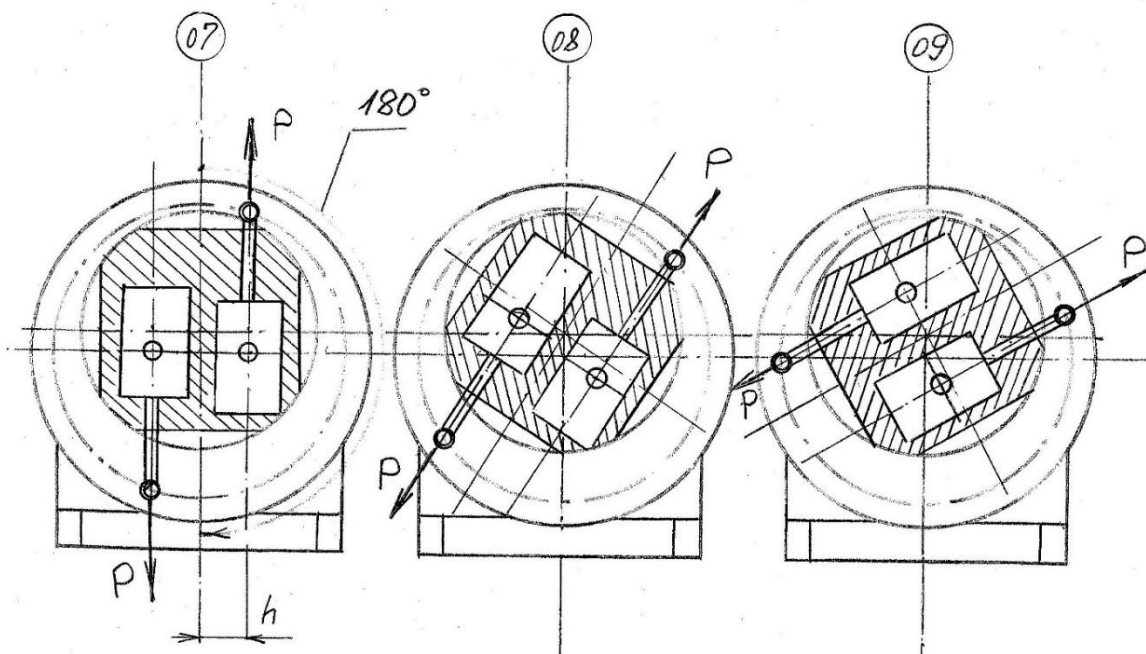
Чертёж позиций поршней и цилиндров роторного двигателя в процессе вращения
